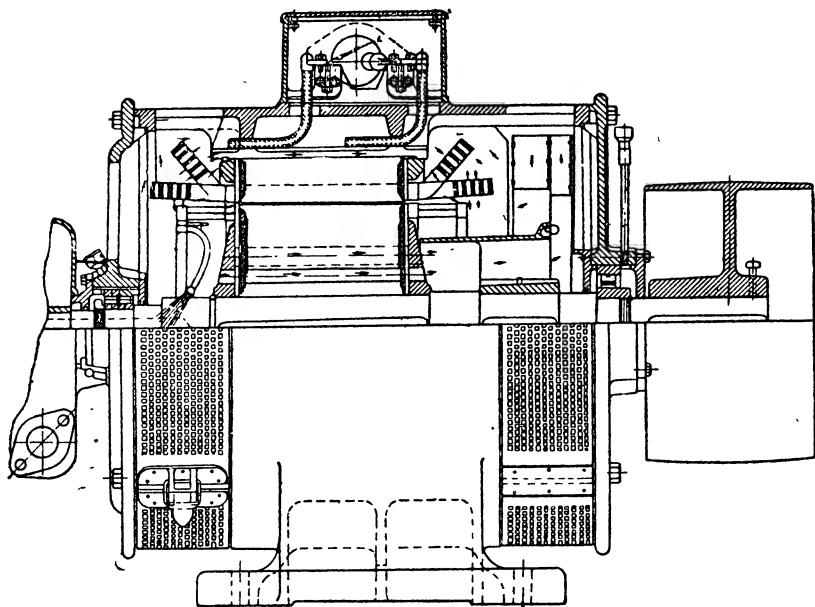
Внешний вид двигателя с воздушным фильтром.
